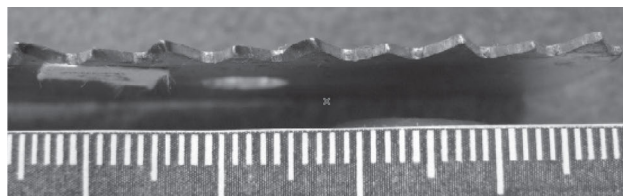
Вид и ширина развода зубцов полотна ножовочной пилы
